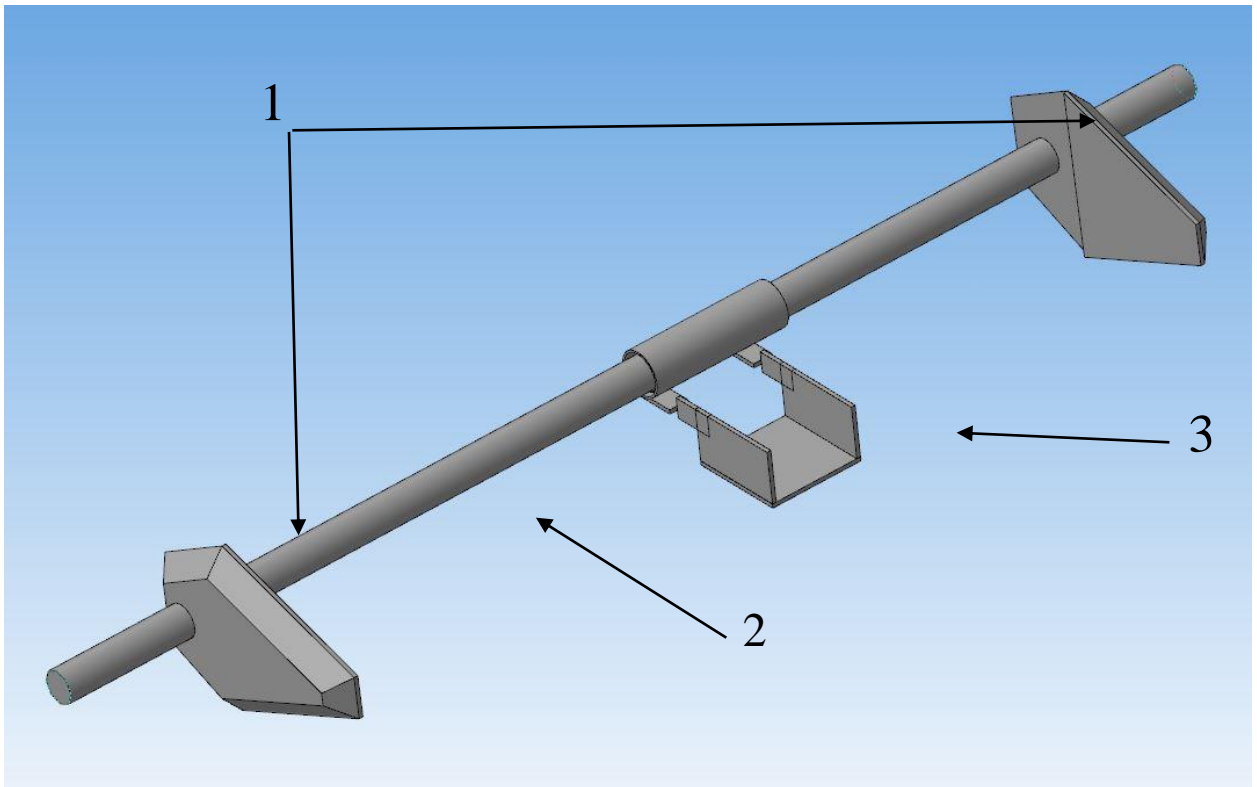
Конструкция механизма для регулировки: 1- прижимы к корпусу; 2 – вал; 3 – крепление сервопривода.
